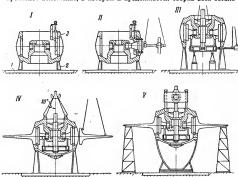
Схема сборки рабочего колеса крестовинного типа с кантовкой втулки.
